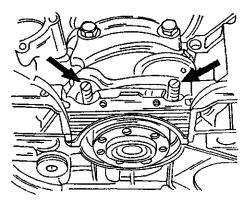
Установка крышки заднего коренного подшипника. Стрелками указаны две ввернутые шпильки. Слева и справа видны две алюминиевые полоски.
